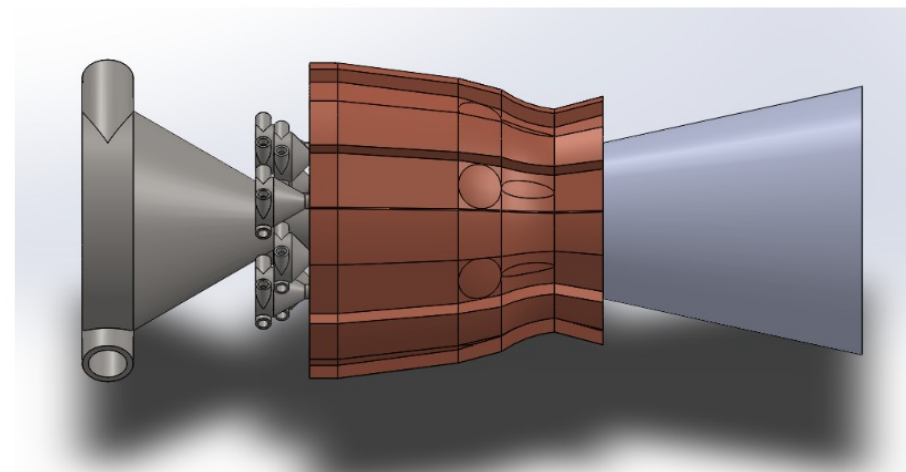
Vista de Perfil da Montagem do Motor com Bocal, Câmara de Combustão e Injetores.
